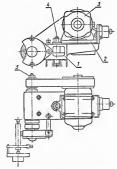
Шлифовальная головка к токарно-винторезному станку 1А62: плита: з — элентродвига-
